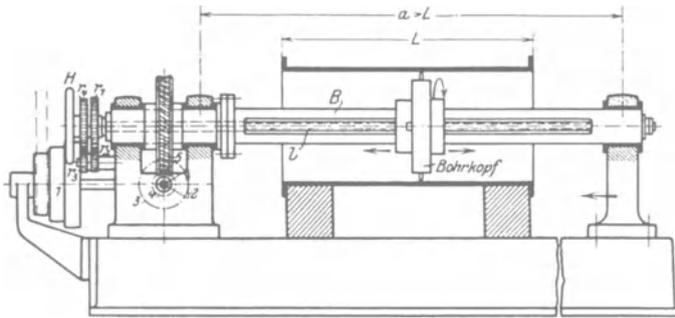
Zylinderbohrmaschine mit wanderndem Bohrkopf.
